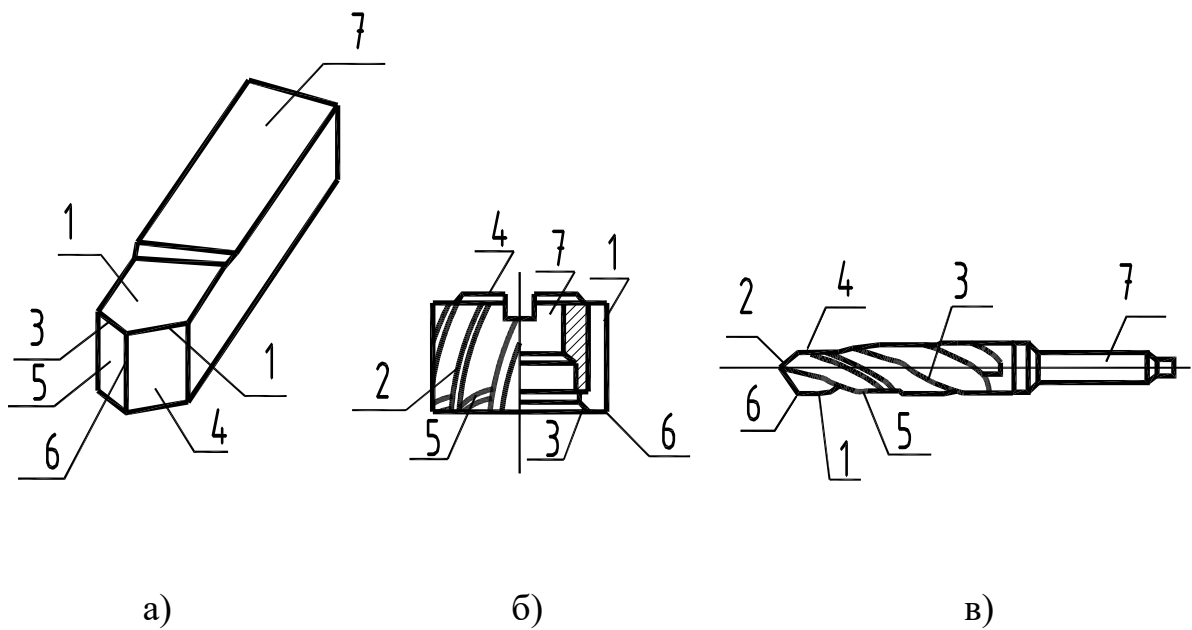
Геометрические и конструктивные элементы режущих инструментов: а) токарного резца; а) фрезы; в) спирального сверла
